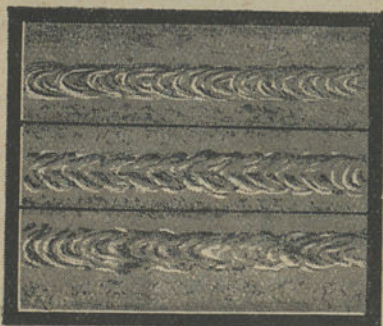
Soldaduras em chapas de 1 mm.
